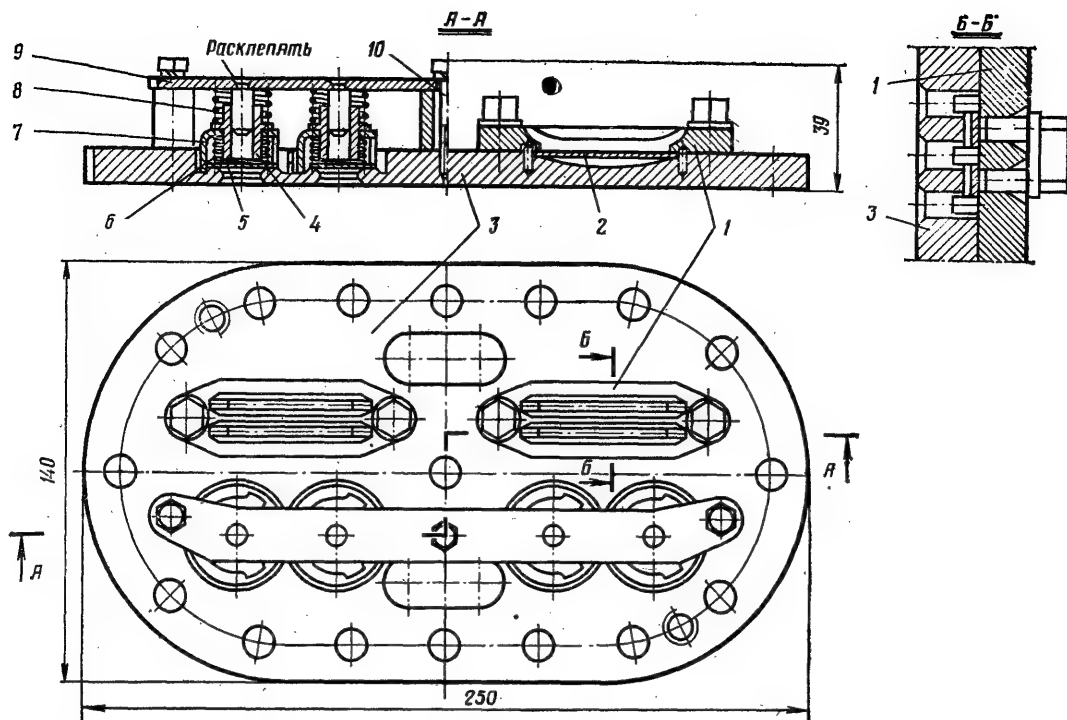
Клапанная плита на двухцилиндровый блок непрямоточного компрессора со всасывающими полосовыми и нагнетательными пяточковыми клапанами:
